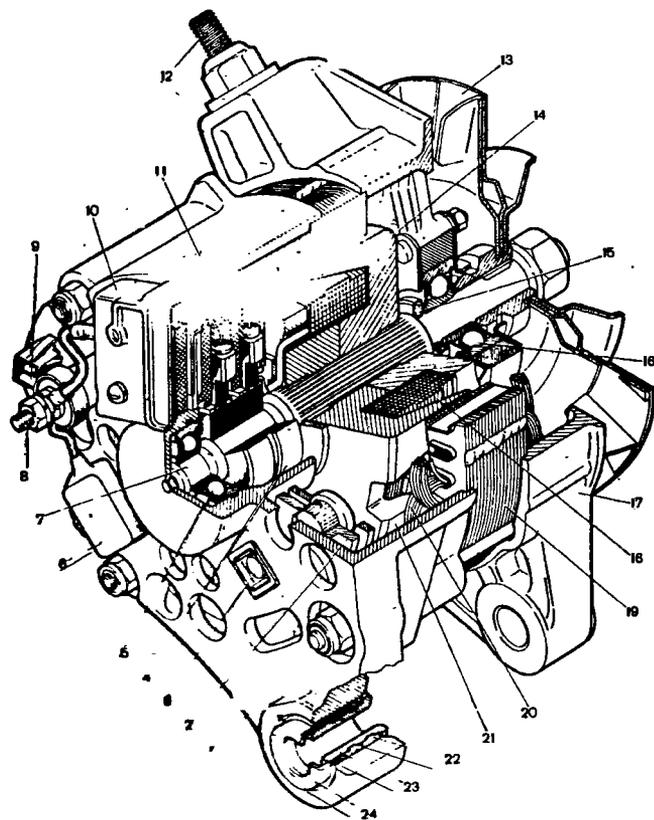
Генератор Г-222: 1 - крышка со стороны контактных колец; 2 - выпрямительный блок; 3 - винт крепления выпрямительного блока; 4 - контактное кольцо; 5 - задний шарикоподшипник; 6 - конденсатор; 7 - вал ротора; 8 - вывод «30» генератора; 9 - штекер нулевого провода; 10 - регулятор напряжения со щеткодержателем; 11 - щетка; 12 - шпилька крепления генератора к натяжной планке; 13 - шкив с вентилятором; 14 - полюсный наконечник ротора; 15 - втулка; 16 - передний шарикоподшипник; 17 - крышка со стороны привода; 18 - обмотка ротора; 19 - статор; 20 - обмотка статора; 21 - полюсный наконечник ротора; 22 - буферная втулка; 23 - втулка; 24 - поджимная втулка
